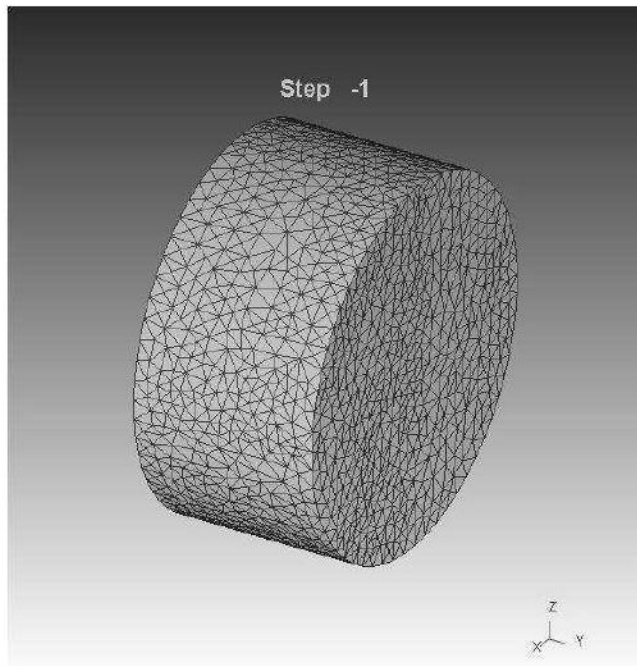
Розбиття заготовки ( $\varnothing = 36$  мм) на 20 000 кінцевих елементів
